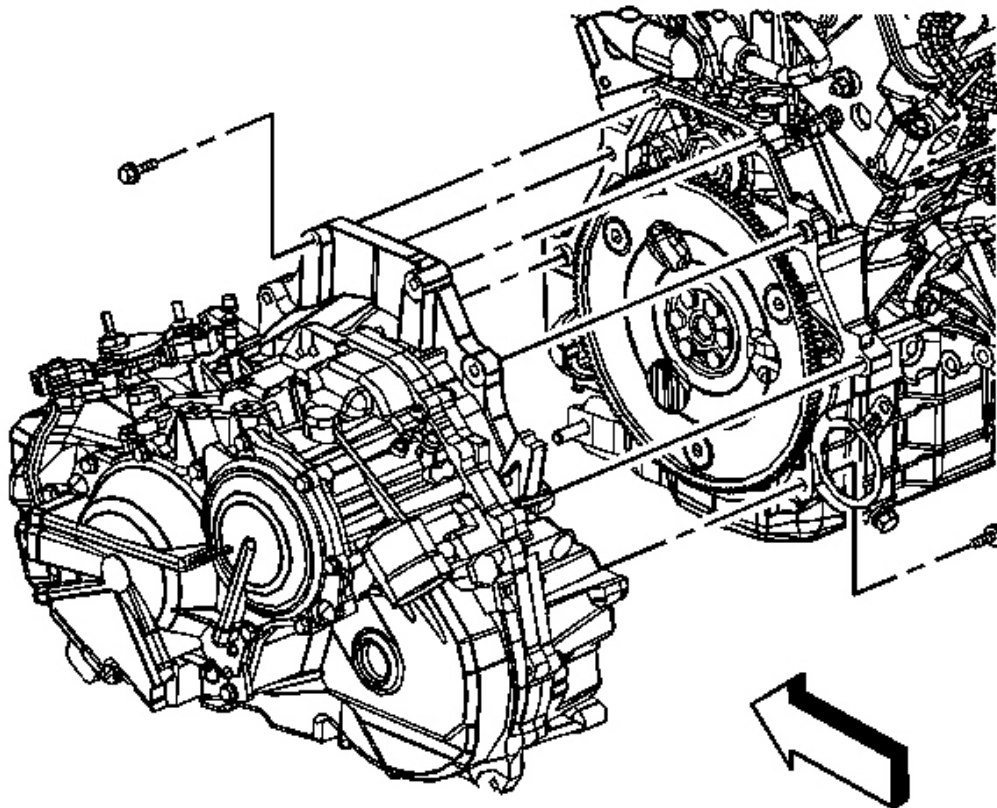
Vista de transeje automático Cortesía de General Motors Corp.
